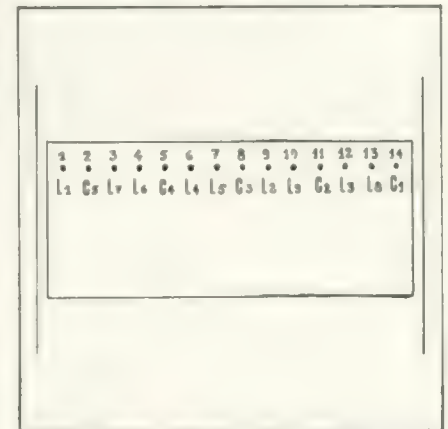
14 points de soudure en ligne très évidents.
